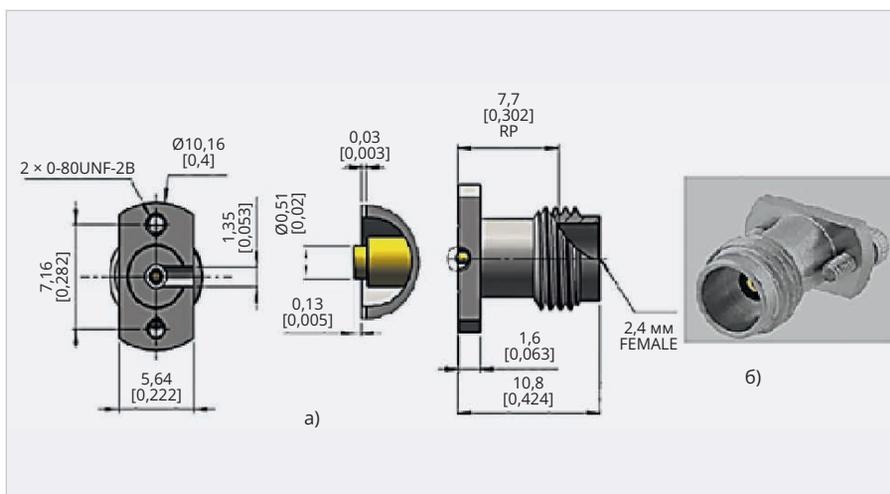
TL-24FD1351F09 – 2,4 мм – прямой соединитель розетка для вертикальной установки на печатную плату: конструкция (а), внешний вид (б)
